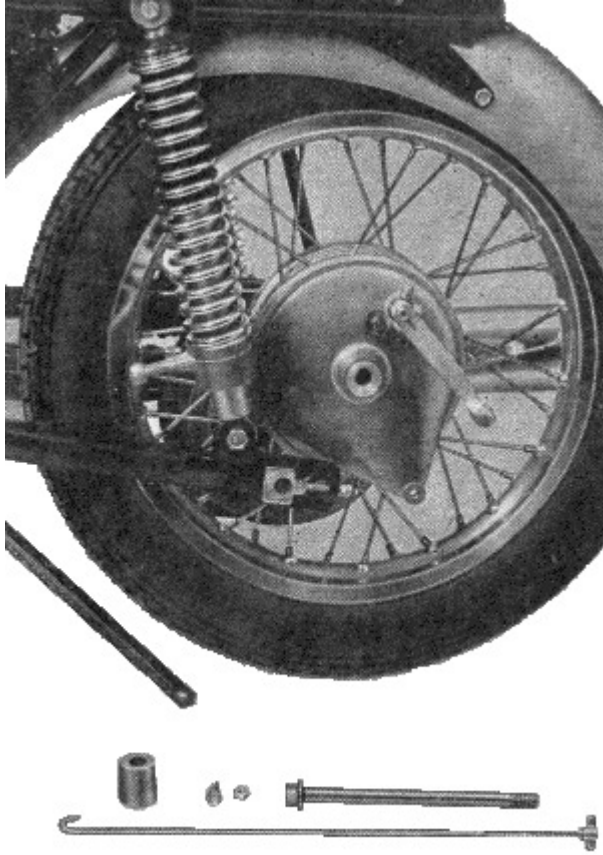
Hinterrad der TS 250/1, vom Antrieb abgezogen
